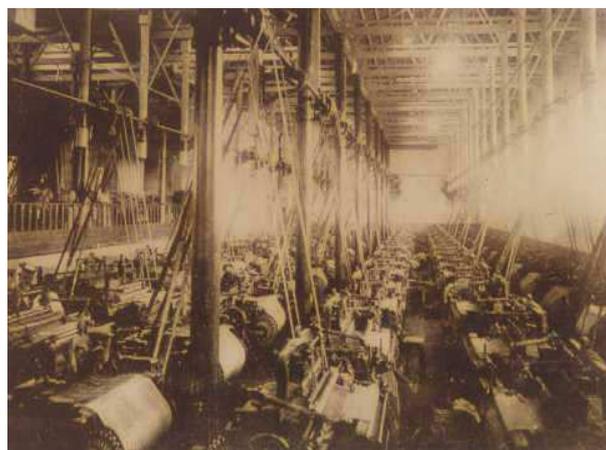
Salões de tecelagem da Fábrica Santa Amélia
